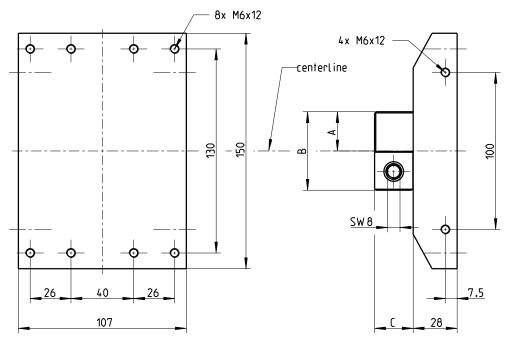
Maschinenadapter mit Spannkeil für Scheibenrevolver mit Direktwerkzeugaufnahme, Typ 9129AD...
